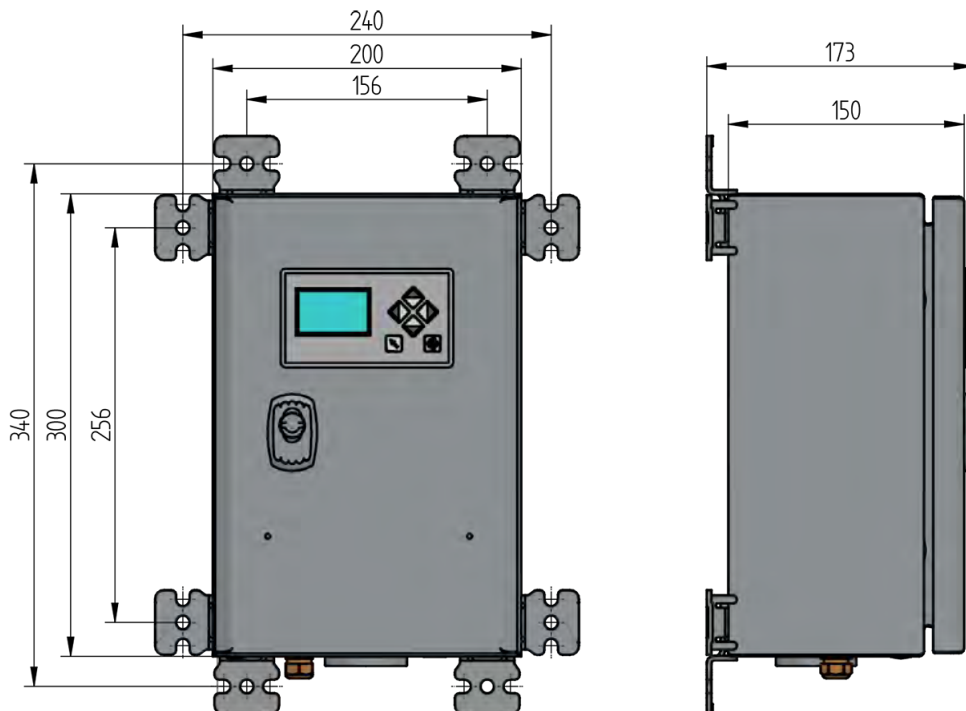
Maßzeichnung Wandaufbaugehäuse für BC300
